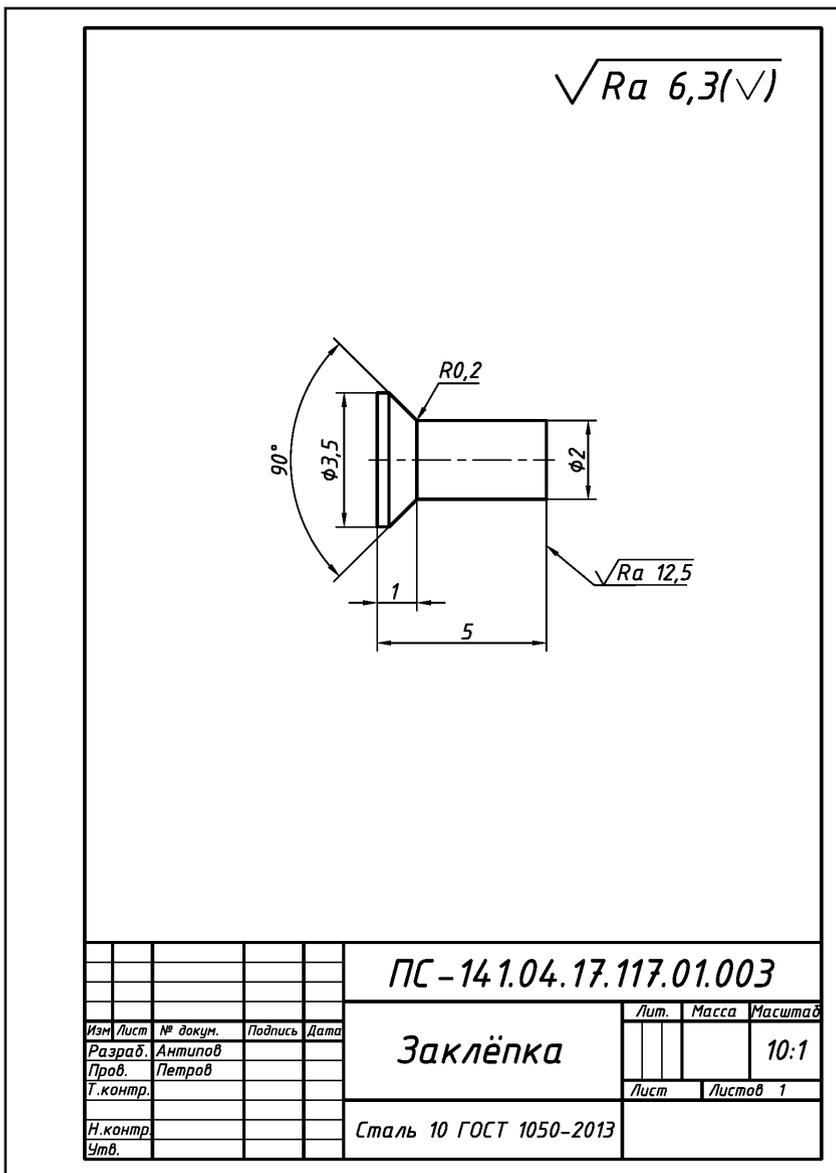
Оформление рабочего чертежа детали «Заклёпка» сборочной единицы «Стойка» (рис. 1.63)
